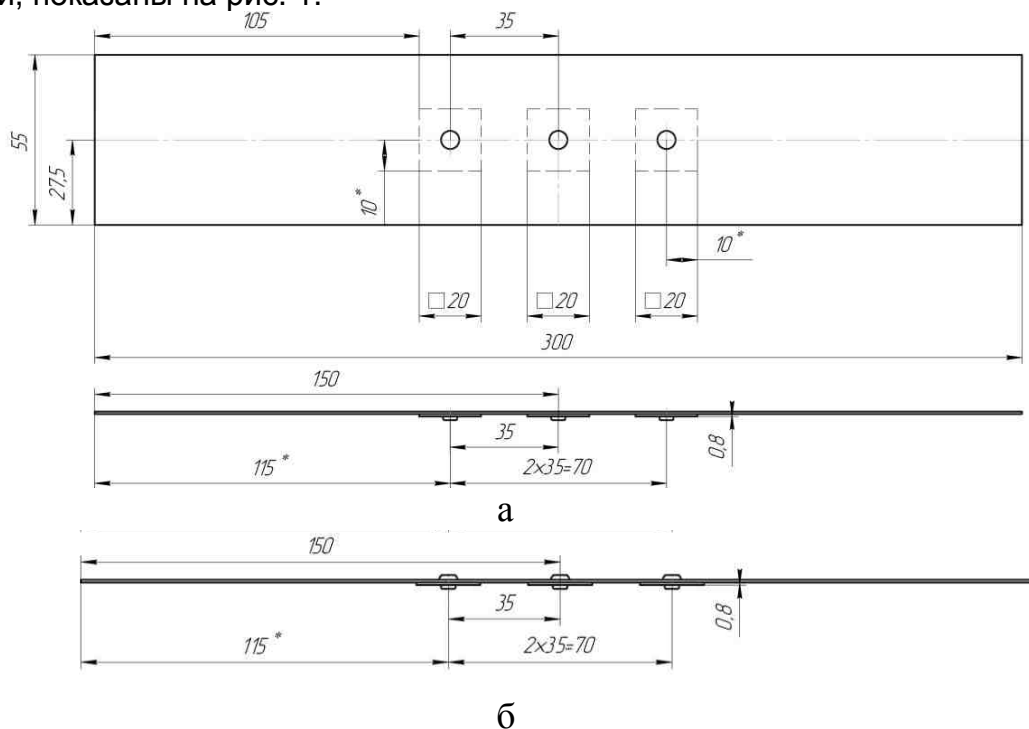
Фрагмент чертежа образцов соединения с тремя накладками: а – с потайными заклепками; б – с заклепками с плоско-скругленной головкой
